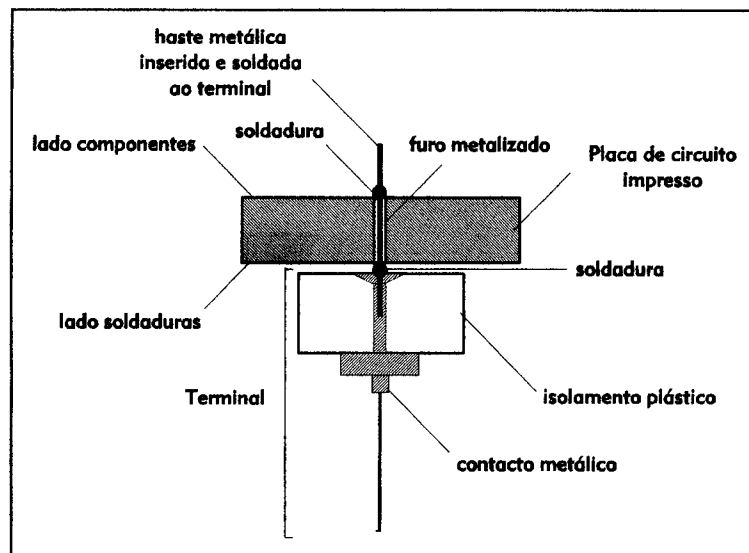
Corte do pormenor da construção e montagem das fichas J2-J3.
